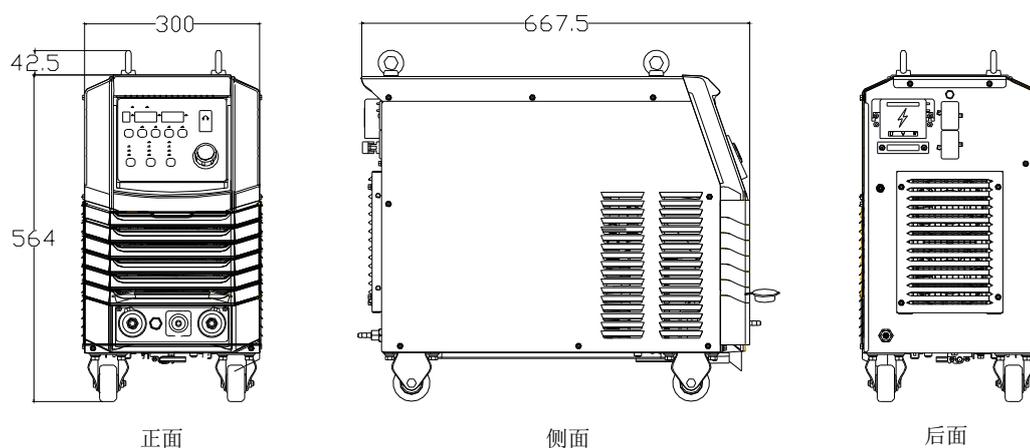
焊接机外观及尺寸（单位：mm）
